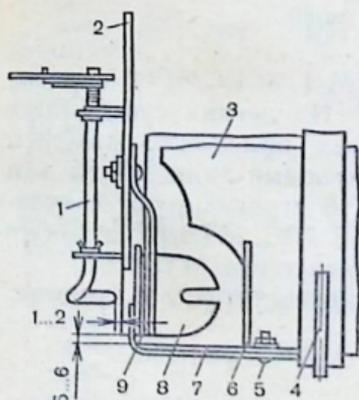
Регулировка вычерпывающего аппарата сажалки:
